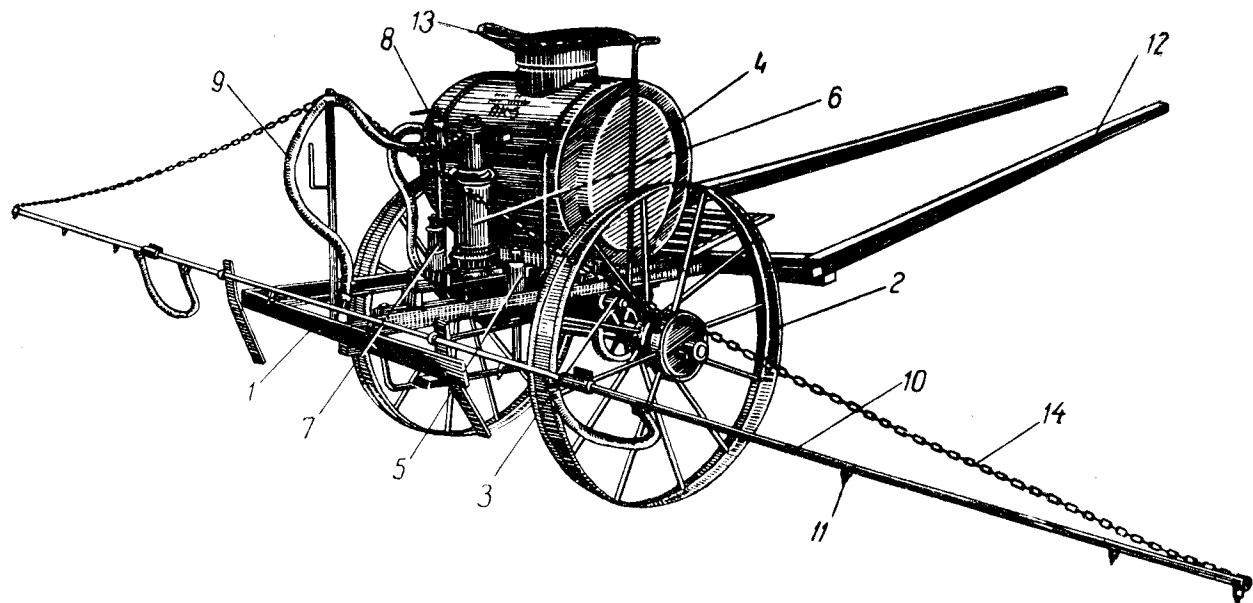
Одноцилиндровый опрыскиватель ОК-5:
